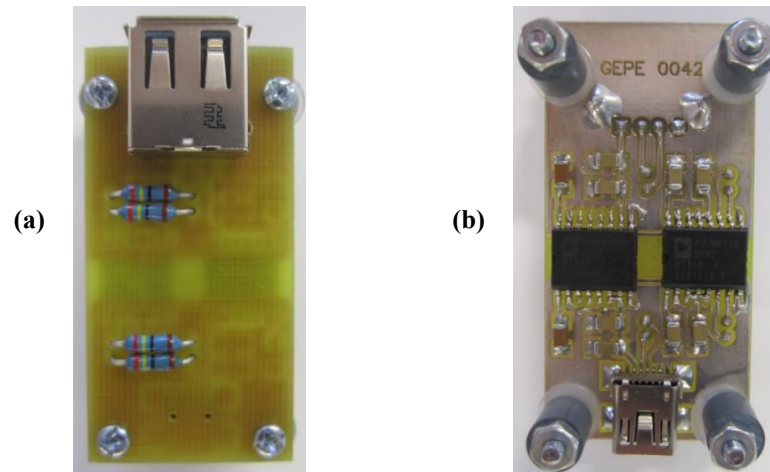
Isolador USB impelmentado em PCB. (a) Vista superior. (b) Vista inferior.
